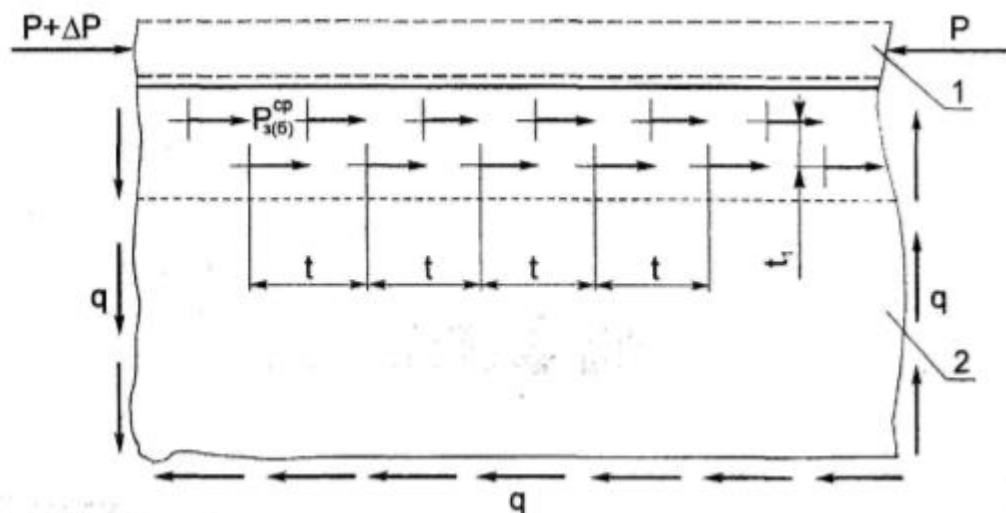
Розрахункова схема заклепувального шва:
